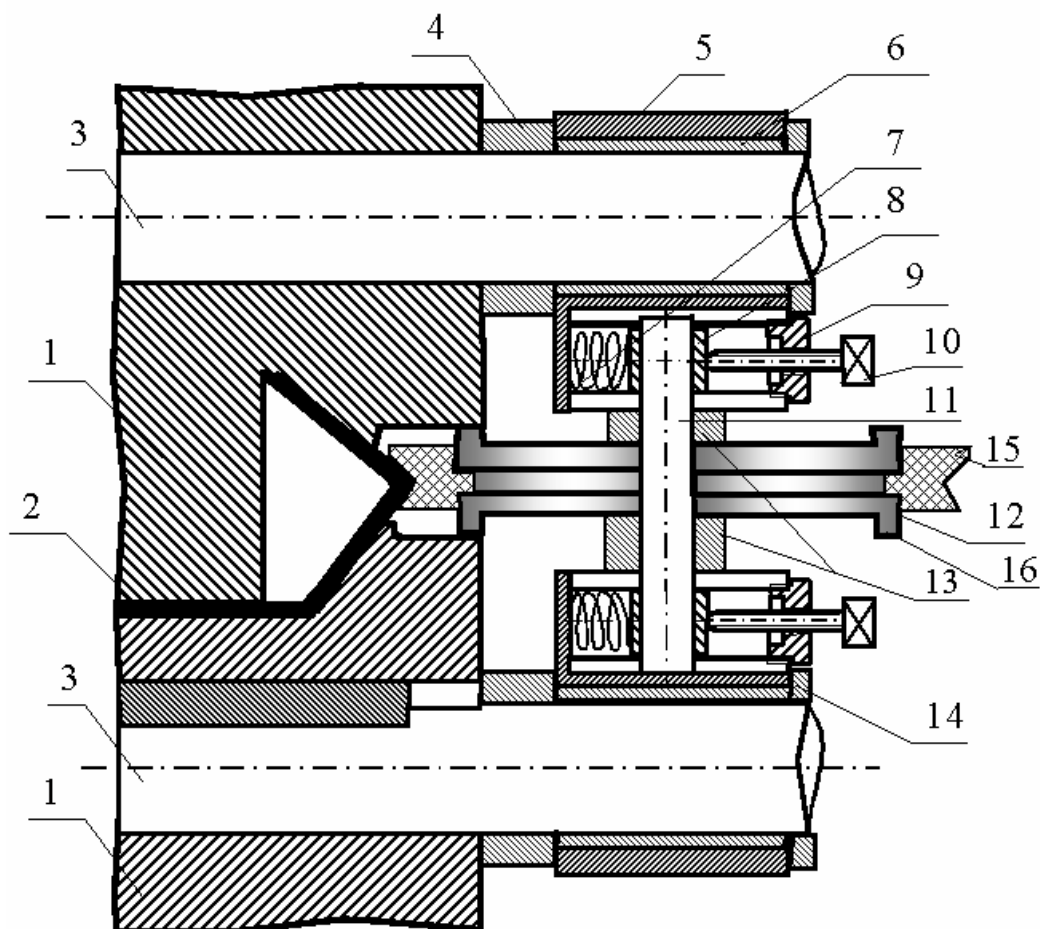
Торцевая проводка: 1 – формующие ролики, 2 – заготовка, 3 – рабочие валы, 4 – регулировочные втулки, 5 – опоры, 6 – бронзовые вкладыши, 7 – пружина, 8 – цилиндрические ползушки, 9 – направляющая пробка, 10 – регулировочный винт, 11 – вертикальная ось, 12 – функциональный ролик, 13 – дистанционные втулки, 14 – регулировочные втулки, 15 – эластичный бандаж, 16 – реборды
